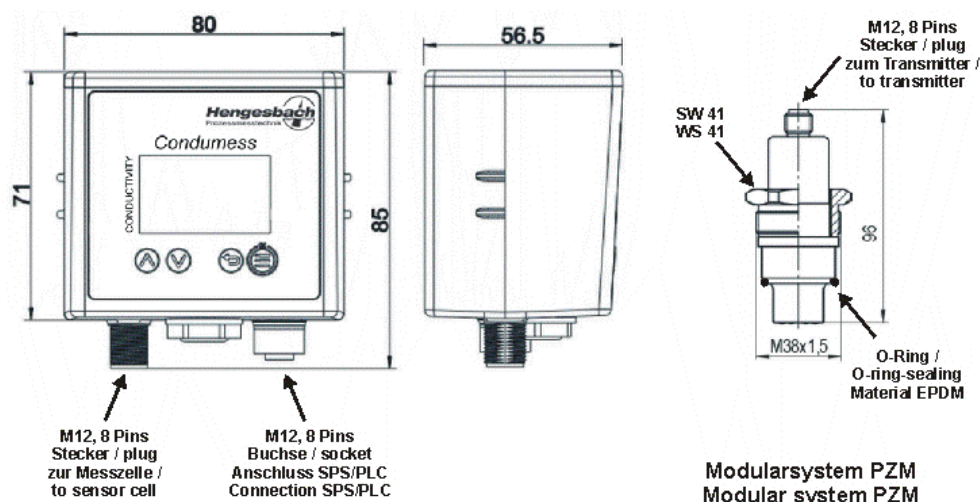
Mechanical dimensions of Condumess (improved model)
